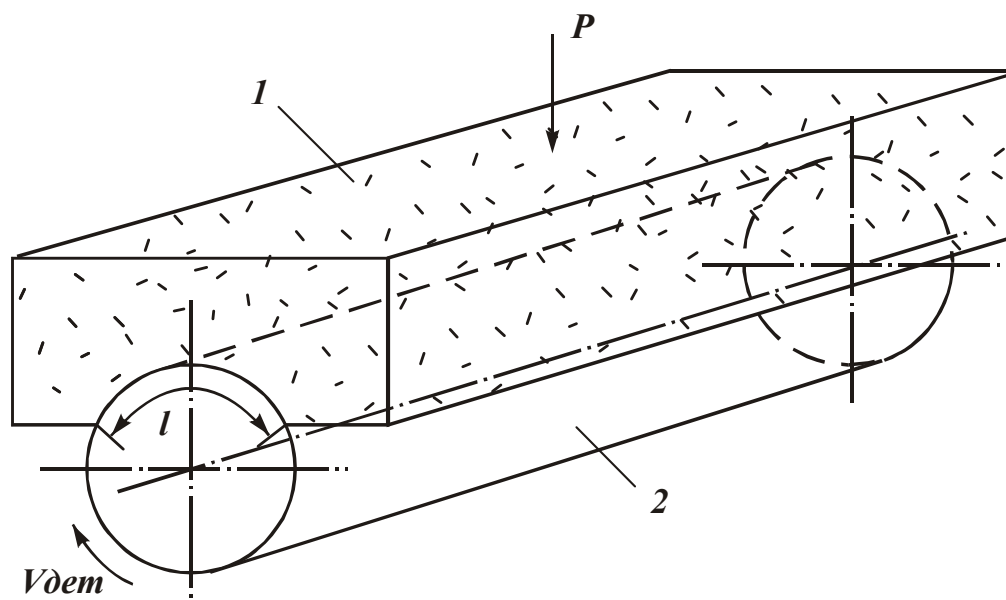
Схема обработки детали абразивным бруском: 1 – брусок; 2 – деталь.
